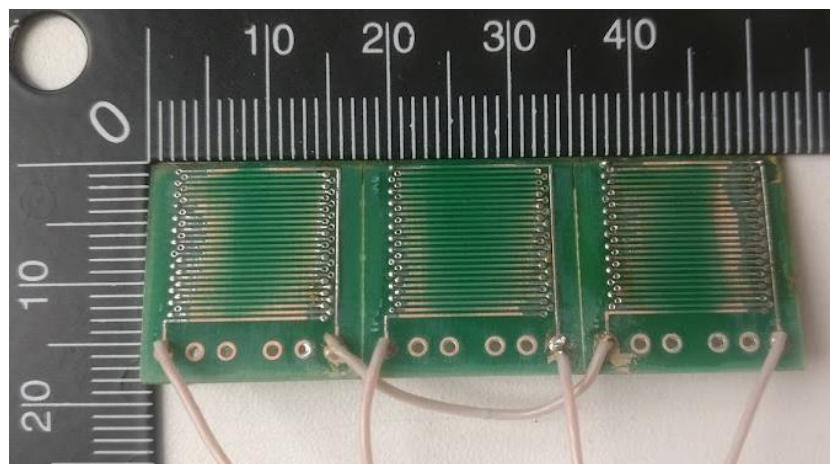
Изготовленный образец 2 RTD-феррозонда
